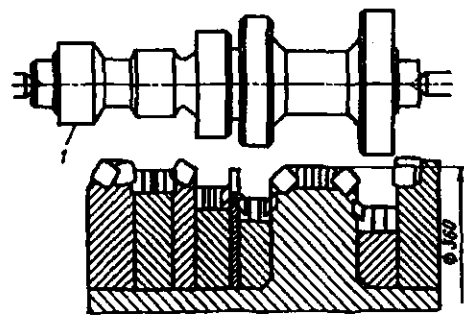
Схема контурного фрезерования ступенчатой детали набором фрез фирмы Хейлилин-цитман (ФРГ): 1 – самоцентрирующий патрон
